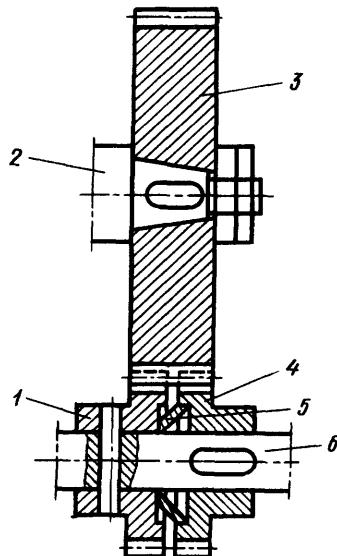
Беззазорная зубчатая передача с выборкой зазора разворотом тарельчатой пружины
